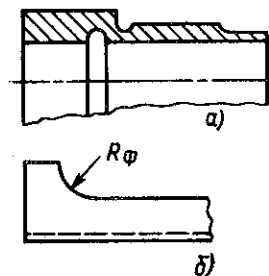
Проточки для выхода резца (а) или фрезы (б)
